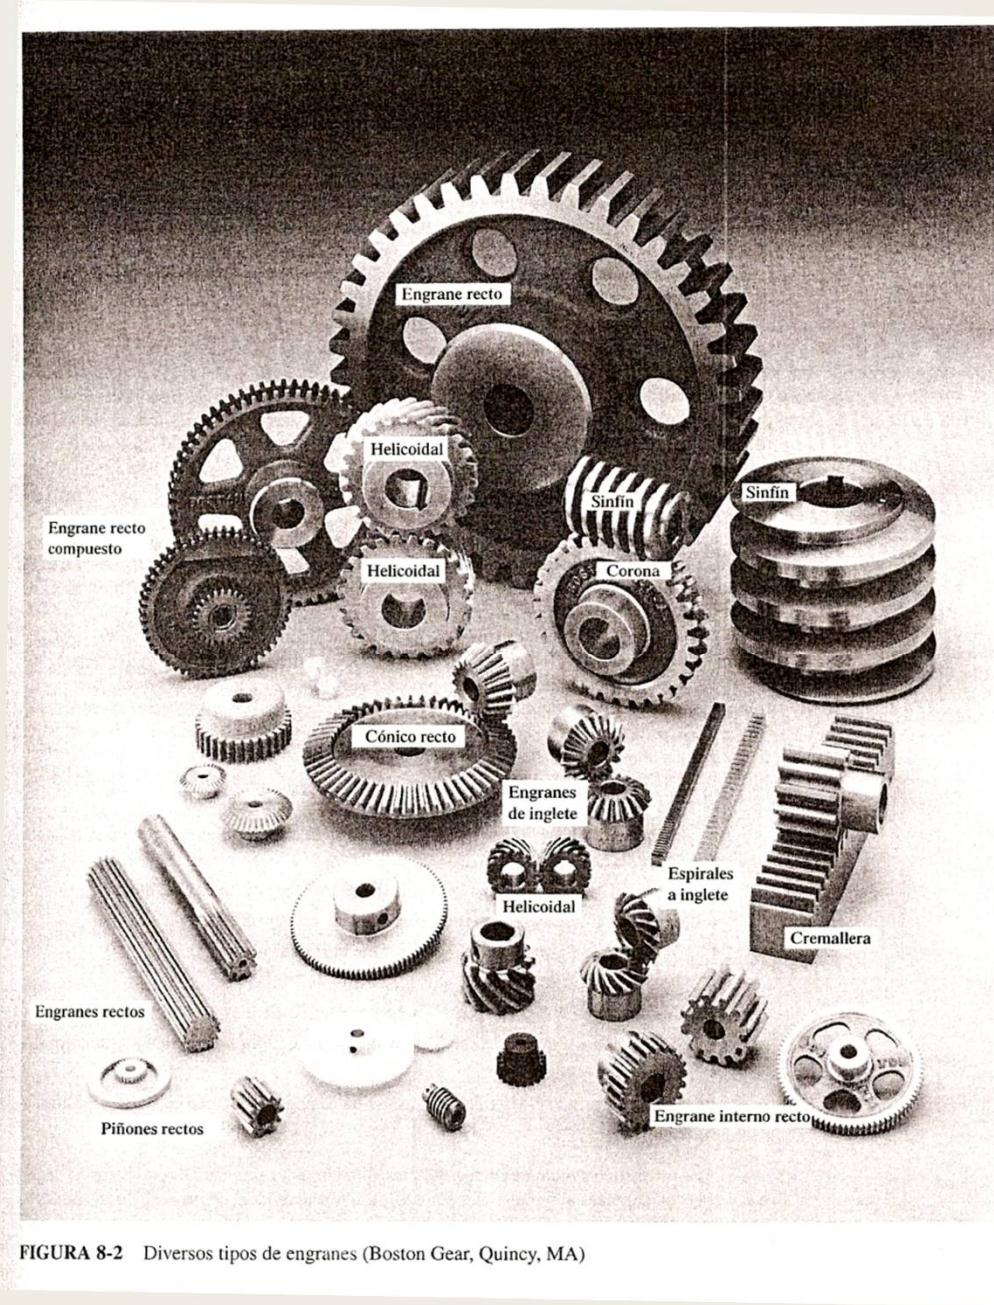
Diversos tipos de engranes (Boston Gear, Quincy, MA)
